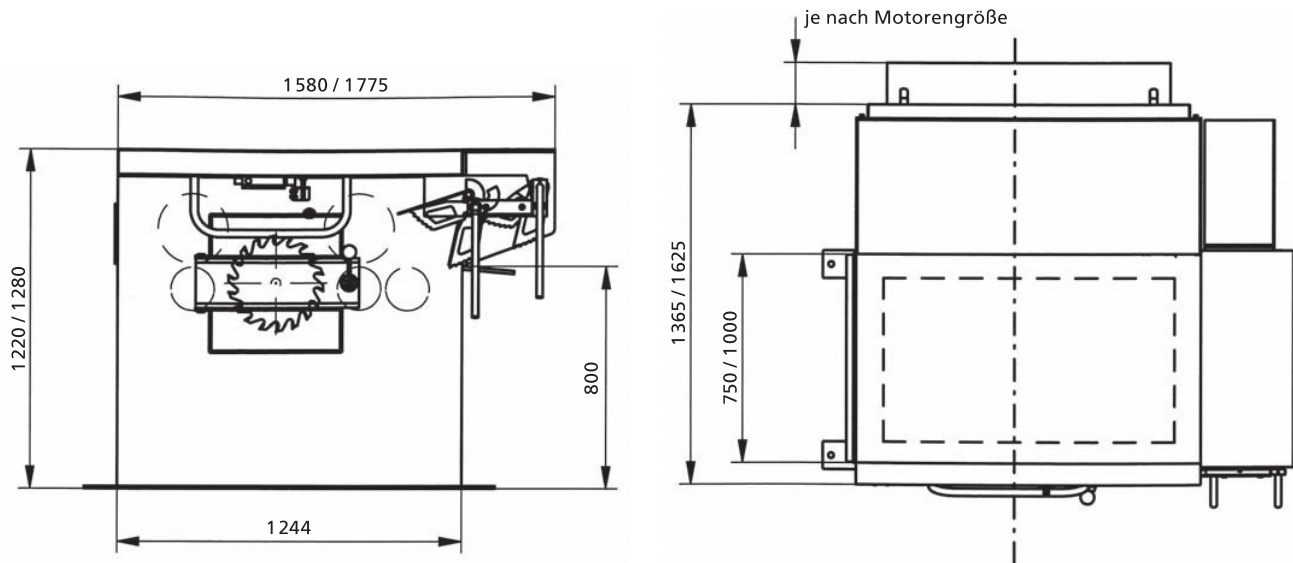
Maschinenabmessungen (mm) einer KME2/BM
